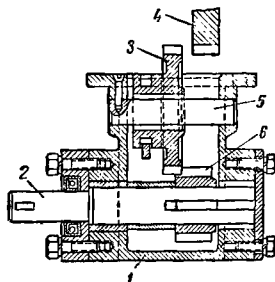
Схема коробки отбора мощности для привода подъемного механизма самосвала автомобиля ГАЗ-93.
